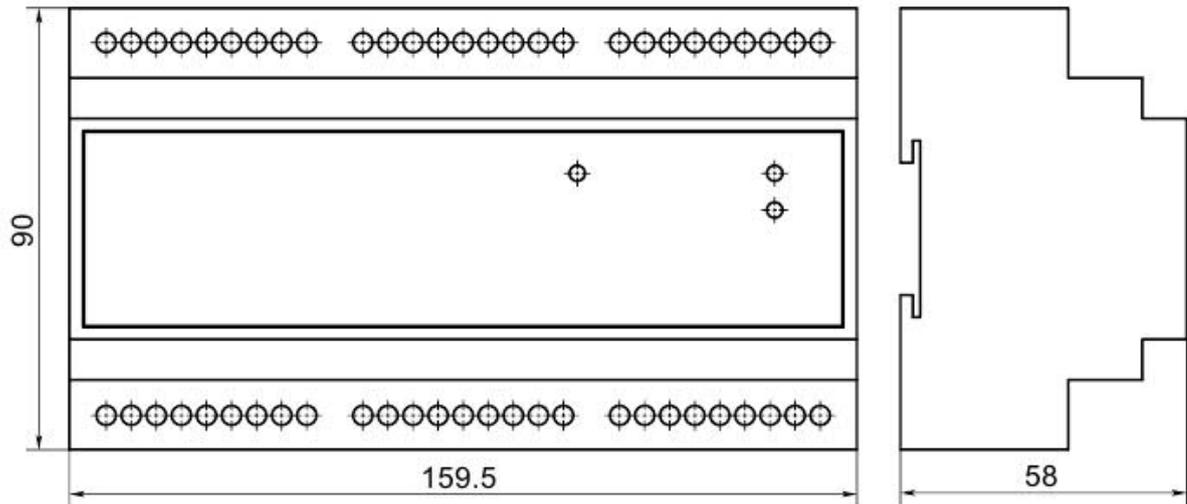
Габаритные и установочные размеры вторичного преобразователя со степенью защиты корпуса IP40 по ГОСТ 14254 и креплением на DIN-рейку
